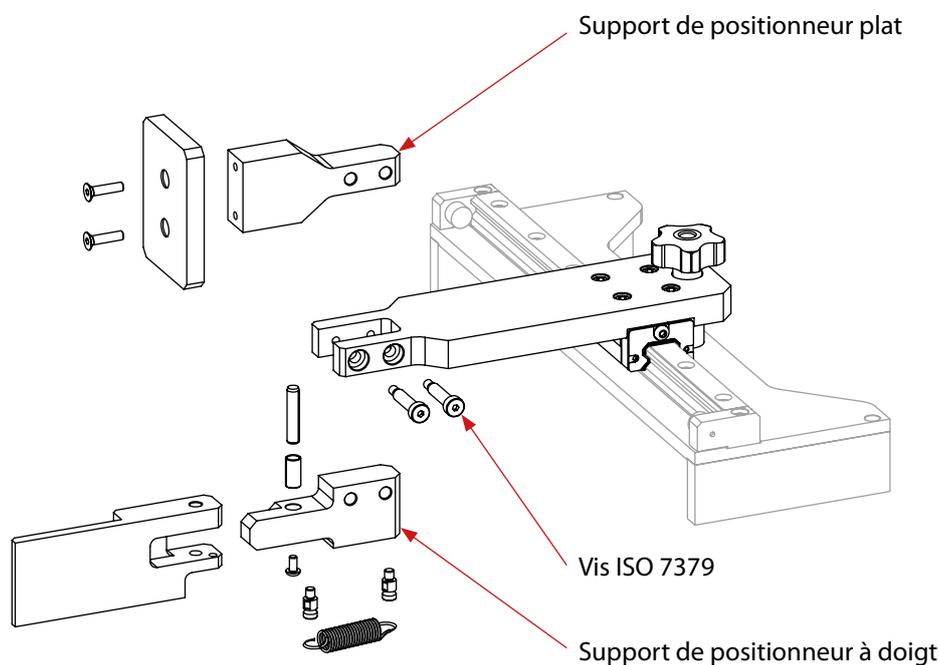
Vue détaillée du montage des deux positionneurs de pièce
